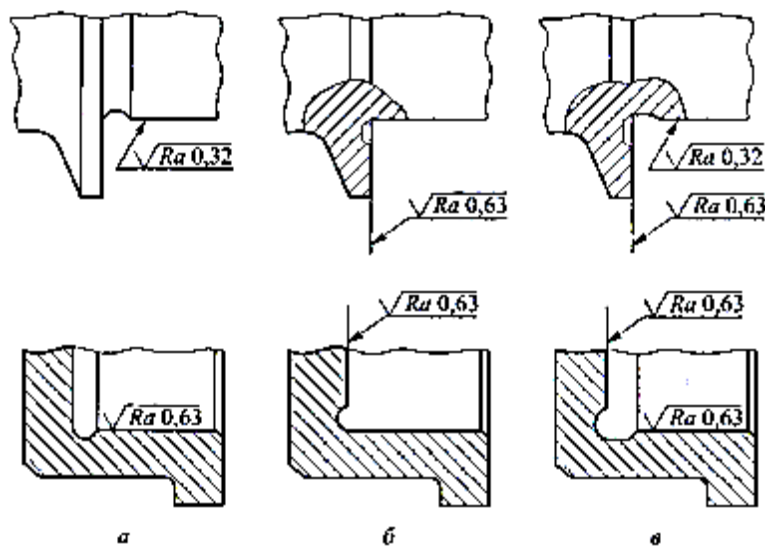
Канавки для выхода режущего инструмента [7]
